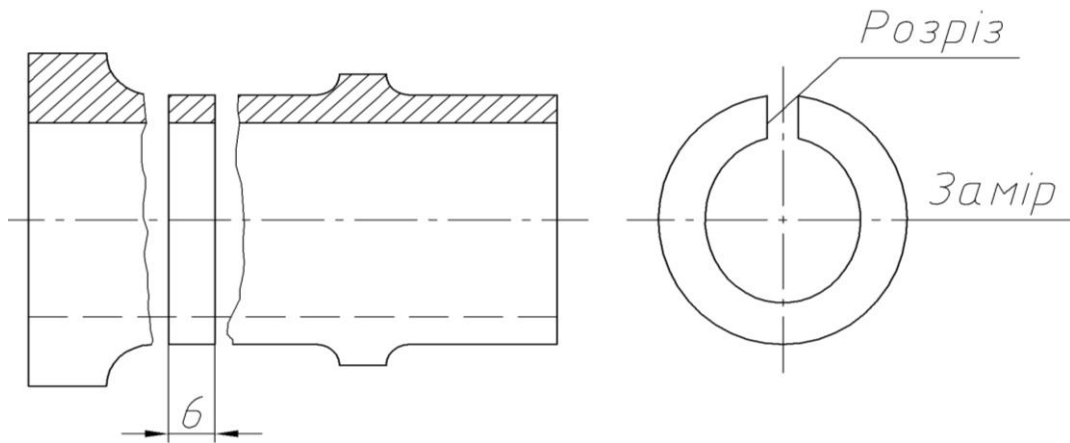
Загальний вигляд зразка гільзи циліндра.
